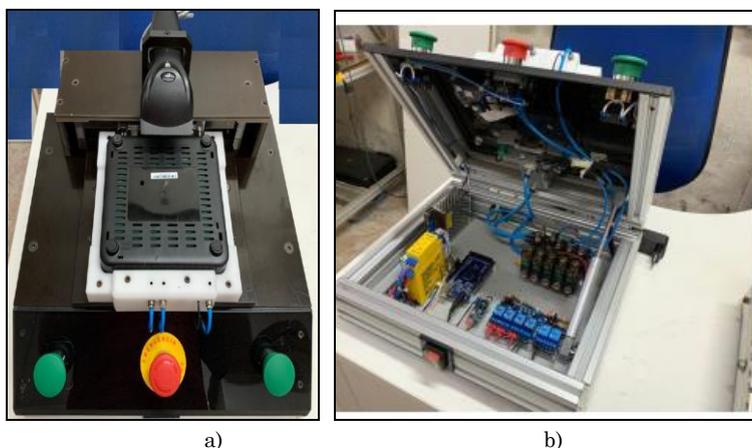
Projeto final do JIG de teste: a) vista superior do módulo, b) dispositivos eletrônicos da parte interna do JIG
